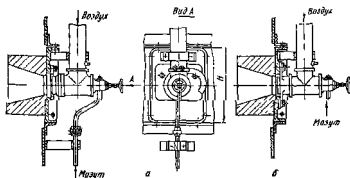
Установка форсунок низкого давления а — с бесфланцевой головкой; б — с фланцевой головкой
